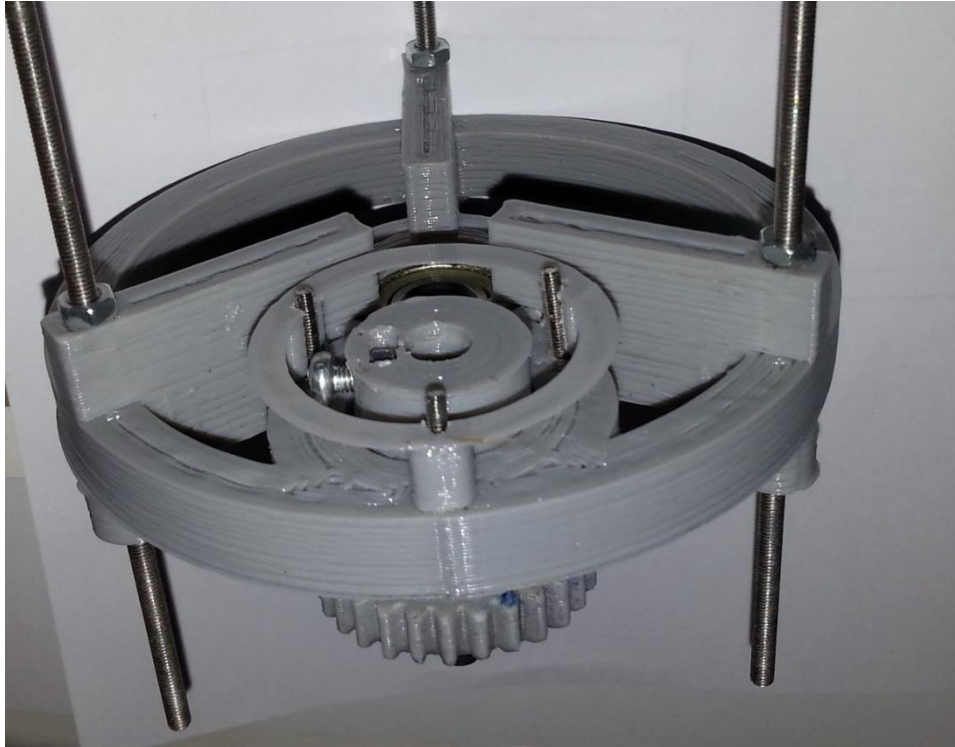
Sistema de engranajes para inmersión. Fuente Propia.
